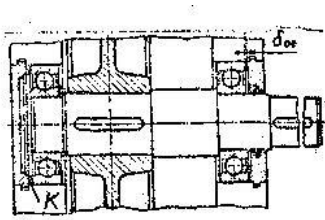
Крепление врезной крышки с установкой регулировочного кольца
